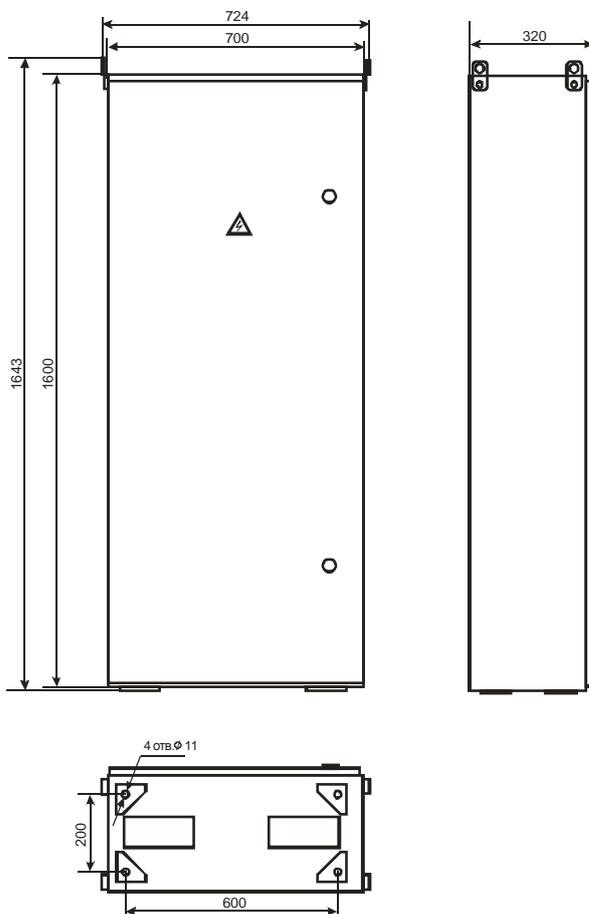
Внешний вид, габаритные и установочные размеры корпуса шкафа силового ШРС1-XX-7-Узола.
